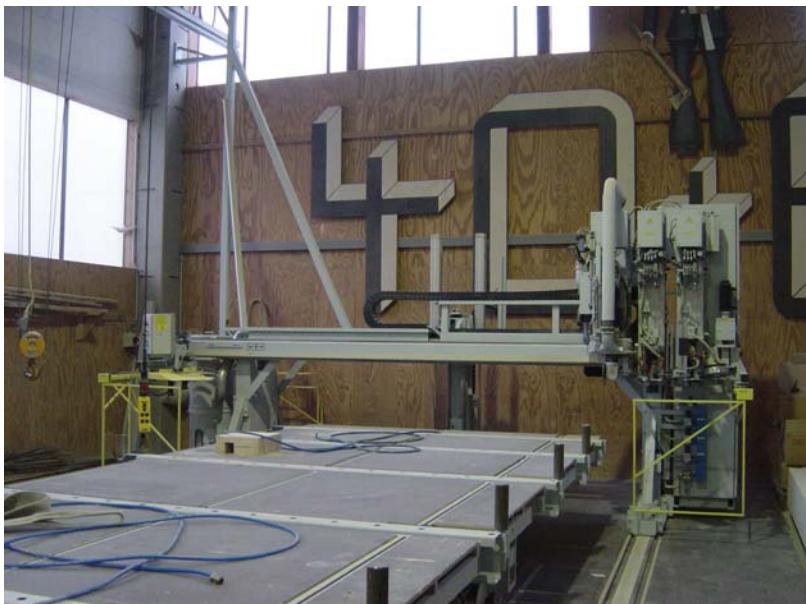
Abbundautomat für Brettstapel-Elemente (Foto Verfasser bei Fa. Merkle)
